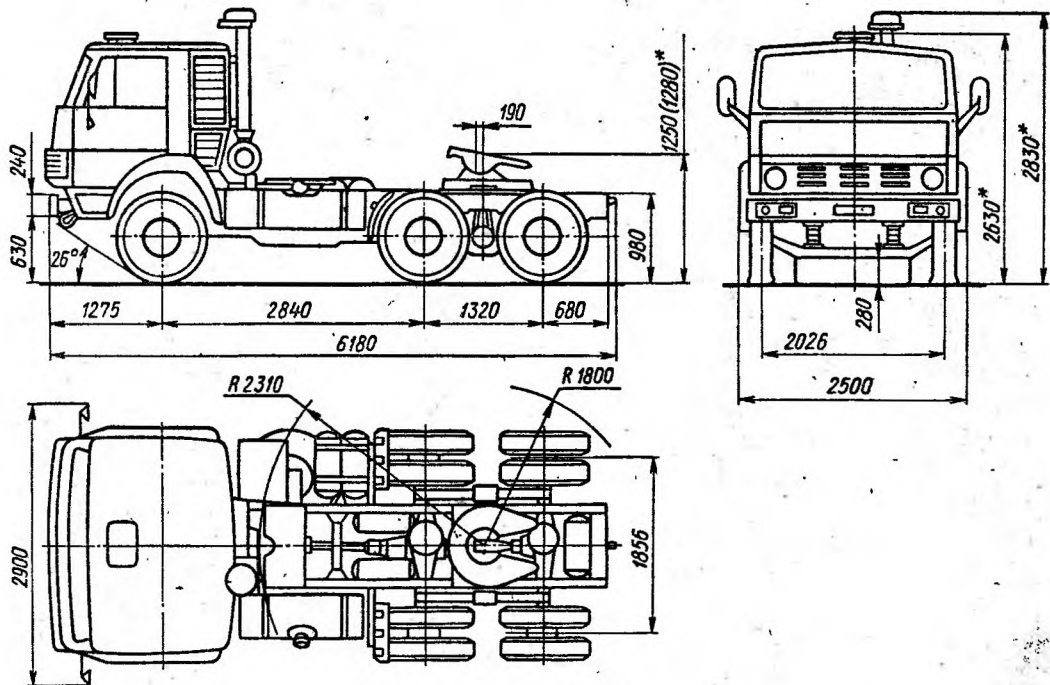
Габаритные размеры автомобилей КамАЗ-5410 и КамАЗ-54112
